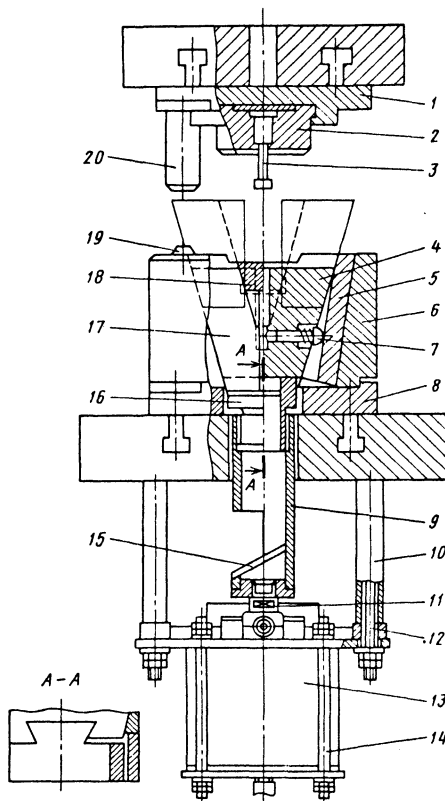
Штамп для закрытой штамповки с вертикальным разъемом матрицы
